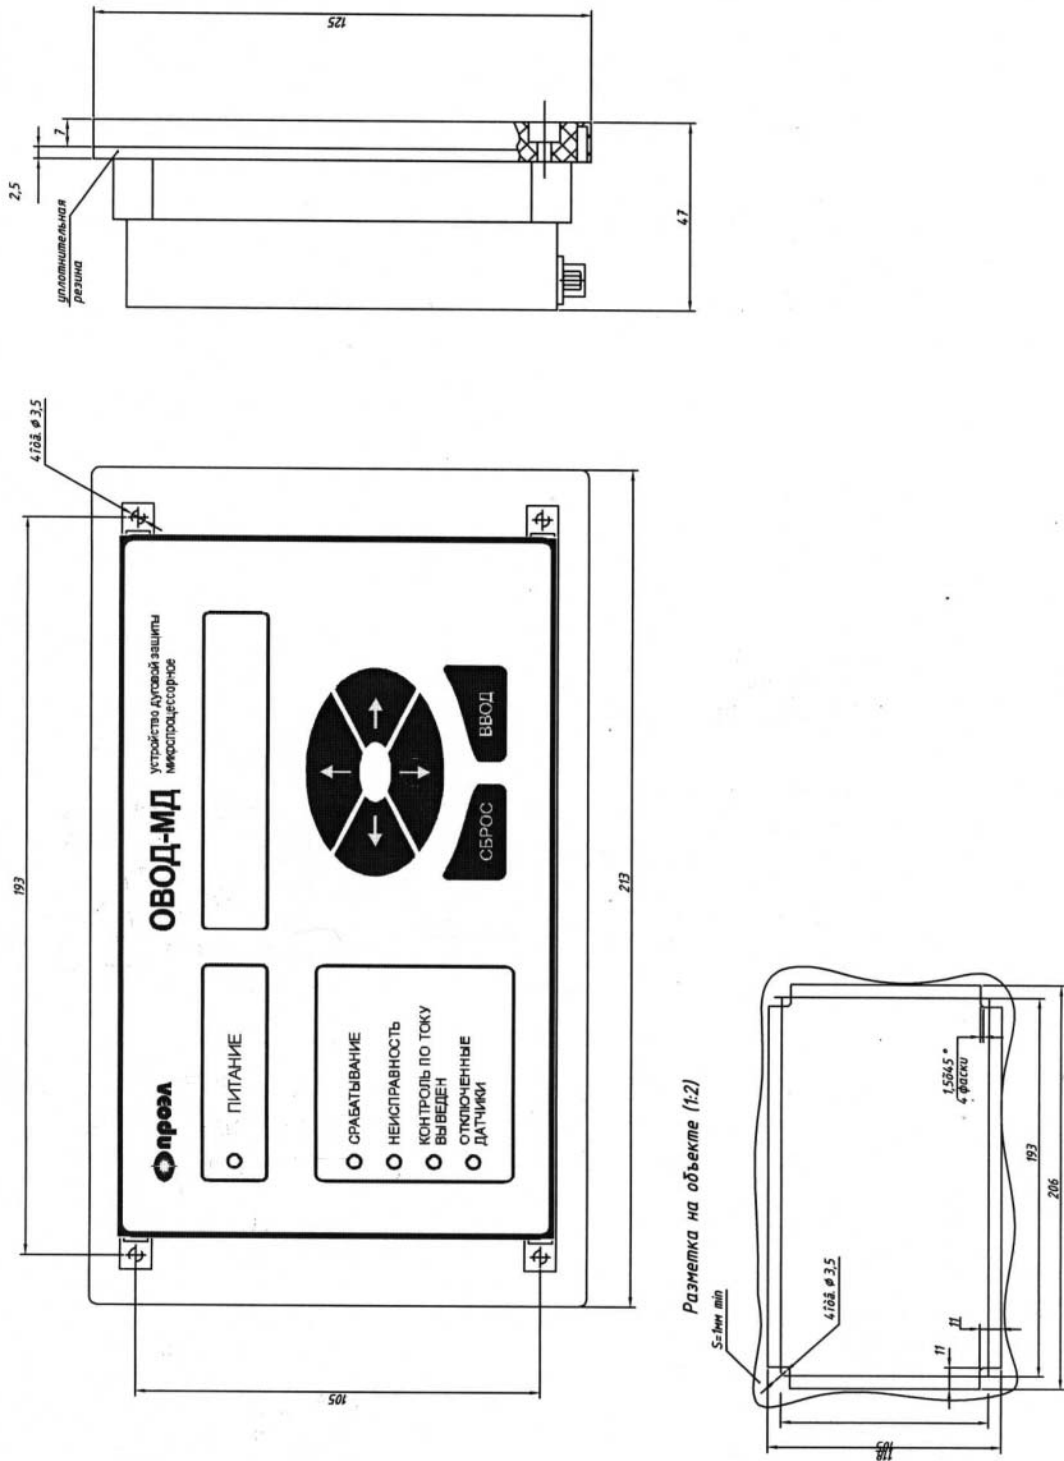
Габаритные размеры блока управления и размеры посадочного места
